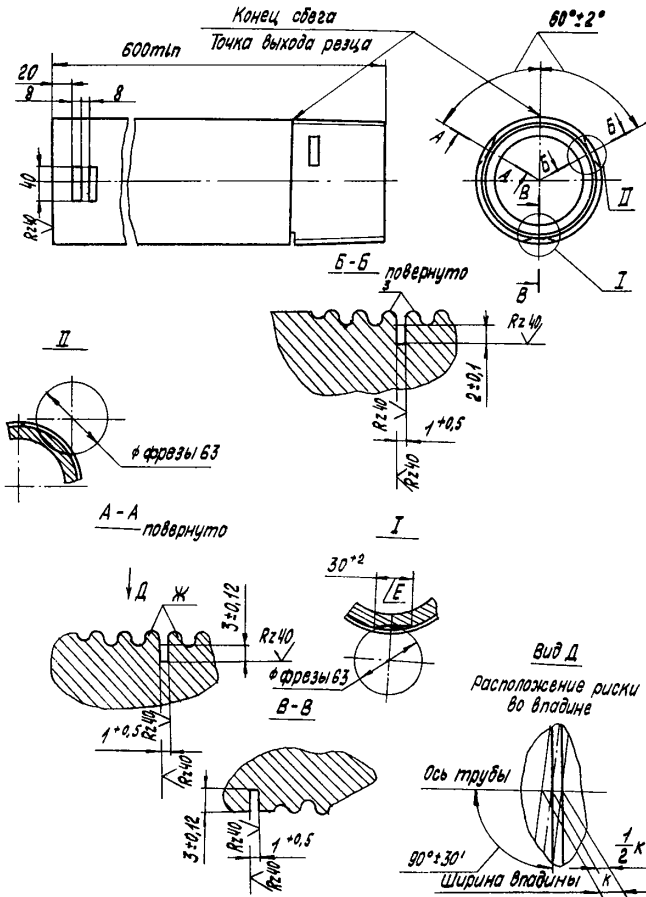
Образец для настройки аппаратуры при контроле резьбы
